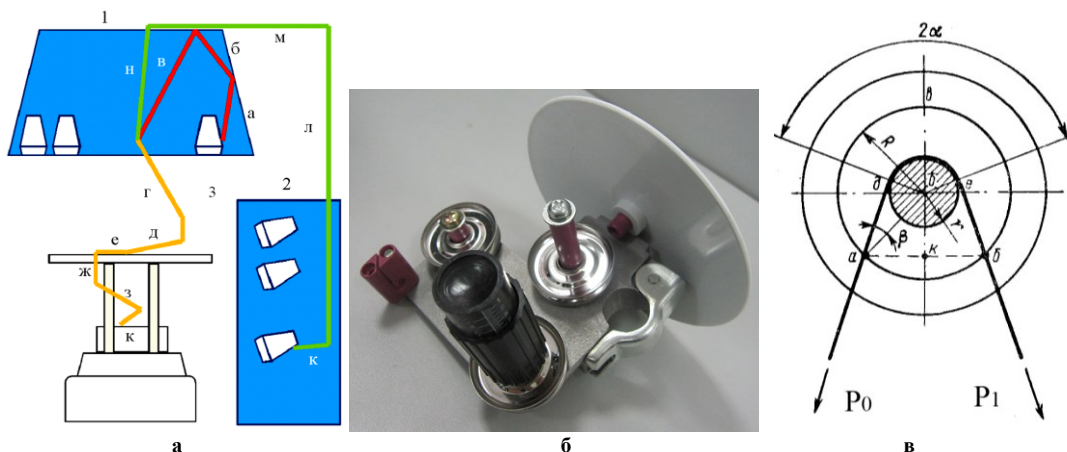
Структурні та розрахункові схеми: а – структурні схеми лінії заправки нитки на круглов'язальній машині; б – шайбовий пристрій для натягу нитки; в – схема для розрахунку натягу шайбового пристрою
